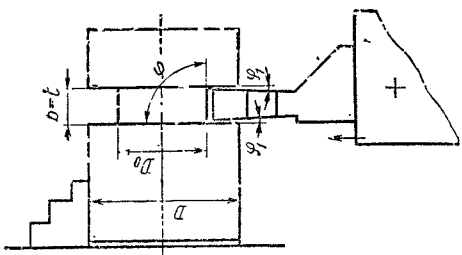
Токарный отрезной резец, оснащенный пластинкой твердого сплава
